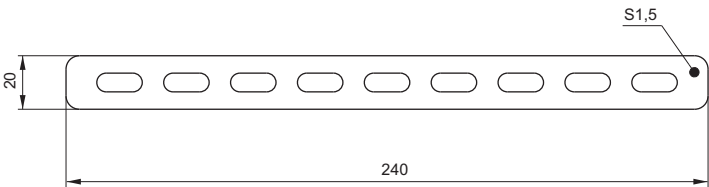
Соединитель перфорированный / Figure B.1 – Perforated connector
